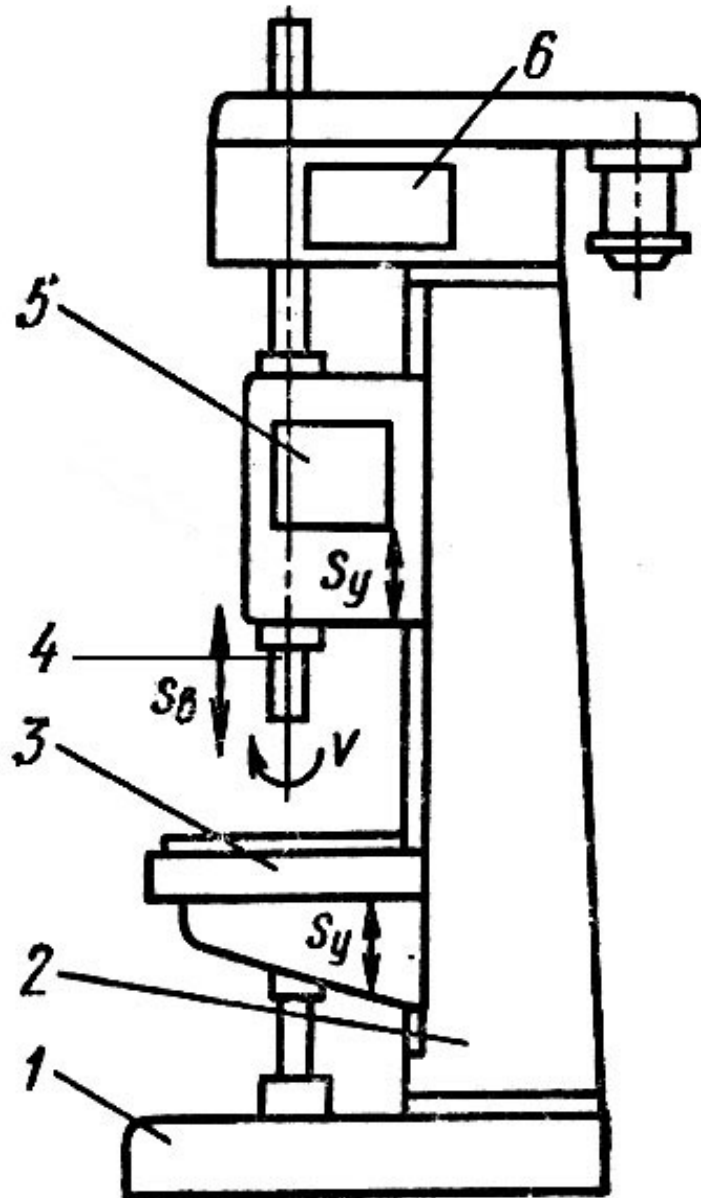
Загальний вигляд вертикально-свердлильного верстату
